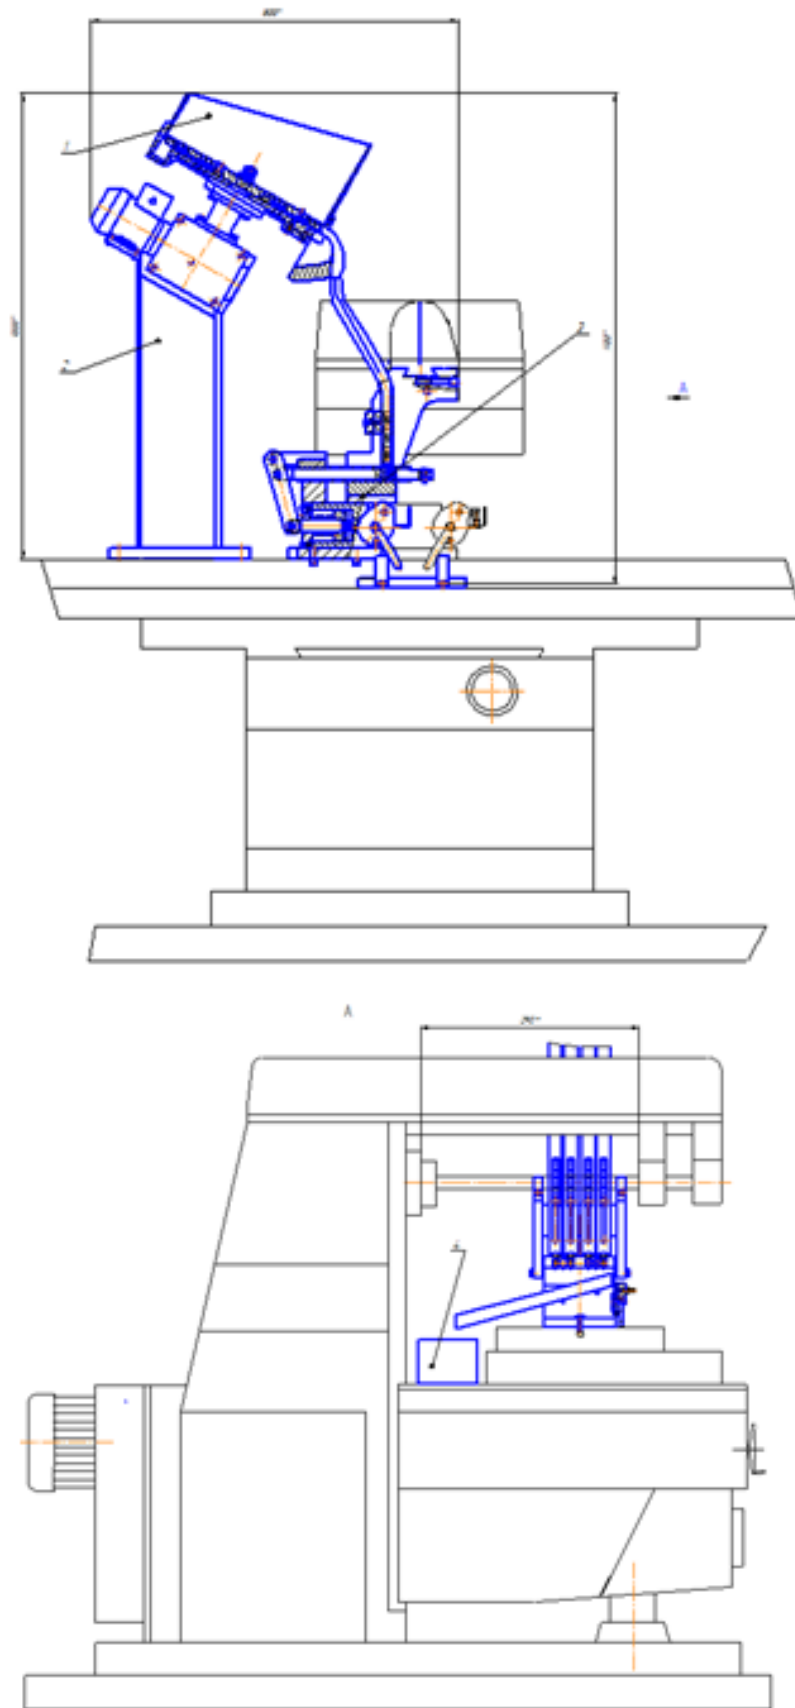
Загальний вигляд автоматизованої системи оброблення шліцевого паза на горизонтально-фрезерному верстаті
